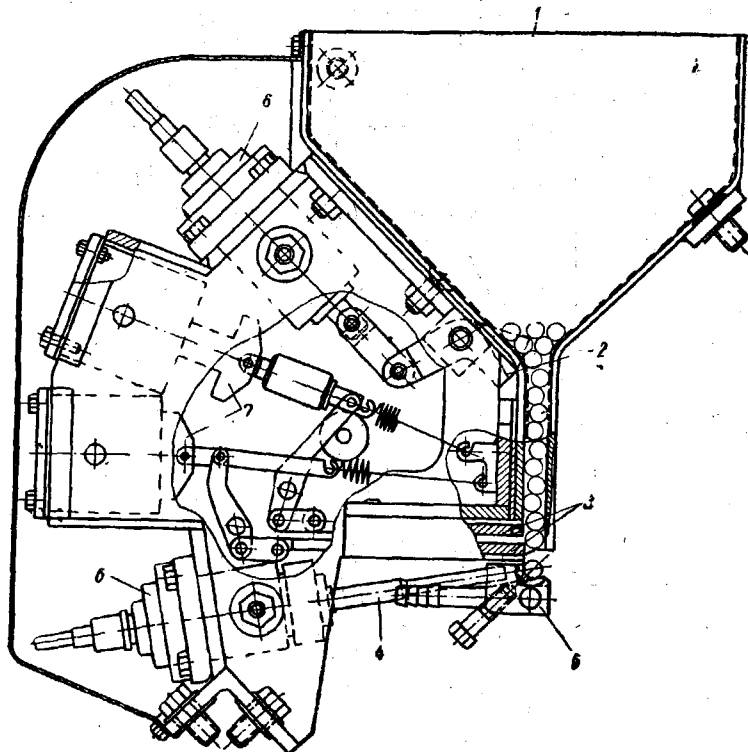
Автомат для сварки сопротивлением цепей:
